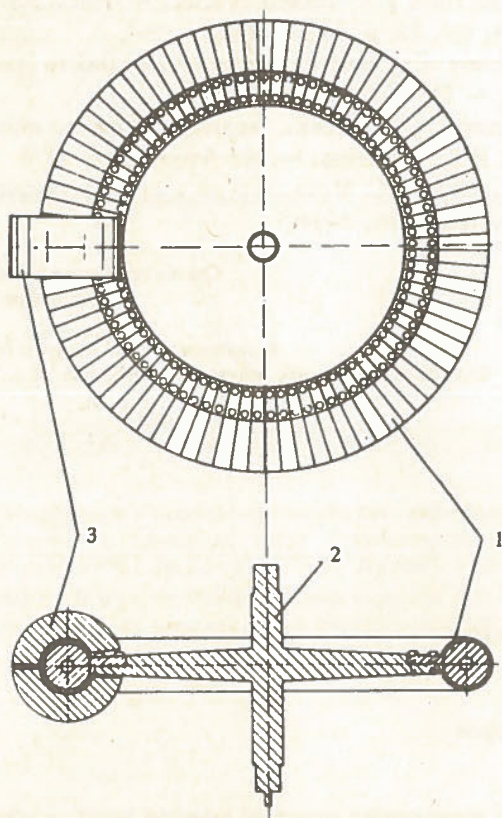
Схематическая конструкция реактора с вращающейся АЗ: 1 — диски из металлического урана; 2 — колесо из стали; 3 — отражатель нейтронов из железа
